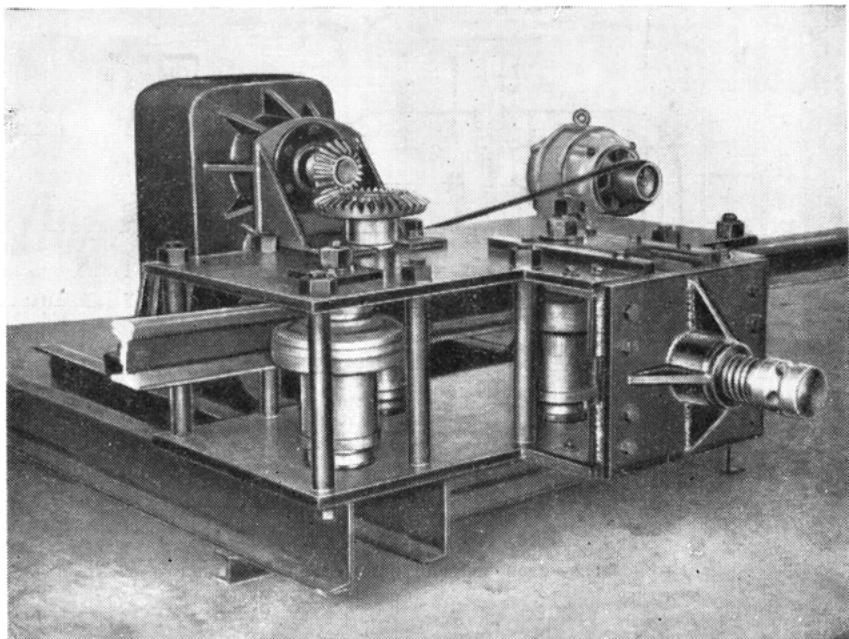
Общий вид четырехроликового пресса для изгибания и выправки рельсов
